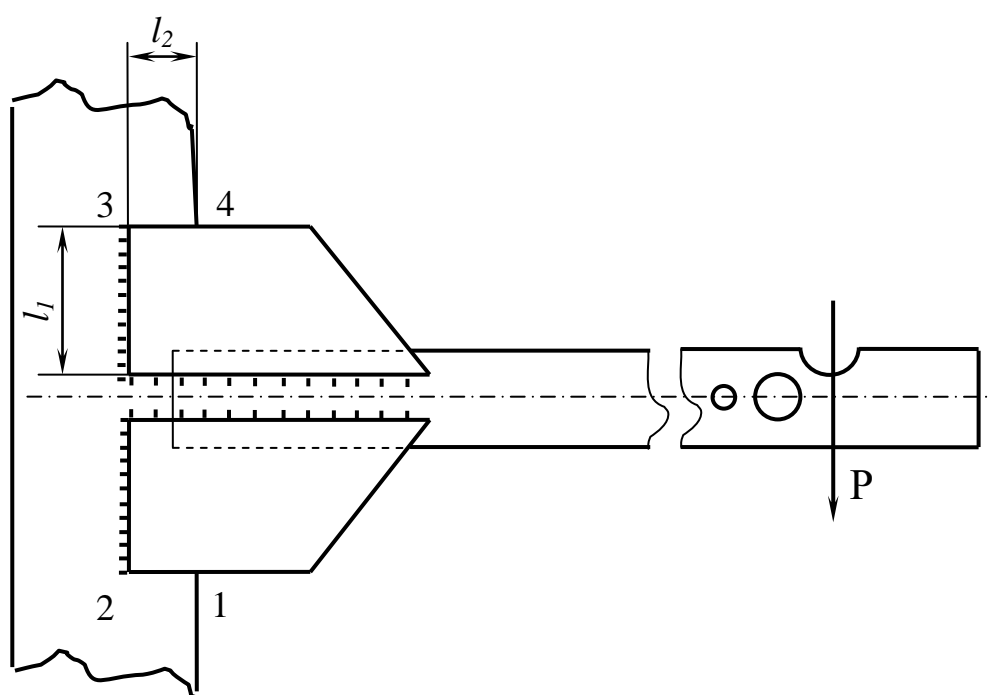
Схема зварного з'єднання тяги і стійки пристосування.
